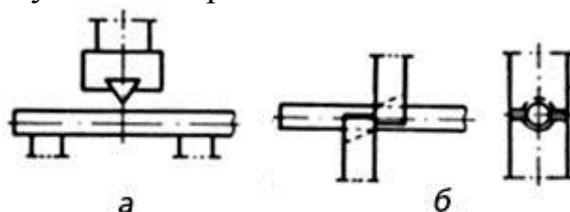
Схема ломки на пресі (а) і різки заготовки ножицями (б).
